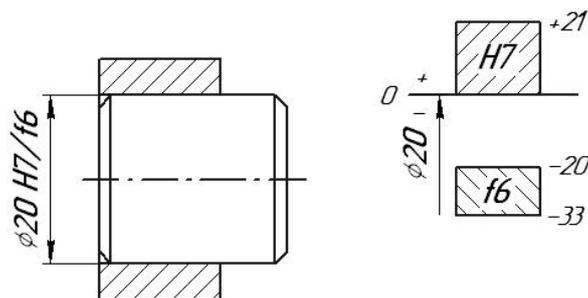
Посадка с зазором и схемы расположения полей допусков
